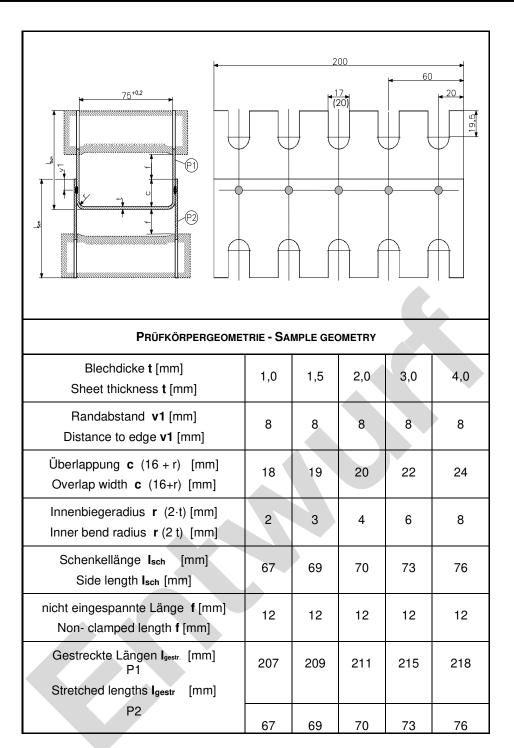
H-Scherzugprobe Widerstandspunktschweißen Figure 9: H-shear lap specimen resistance spot welding
